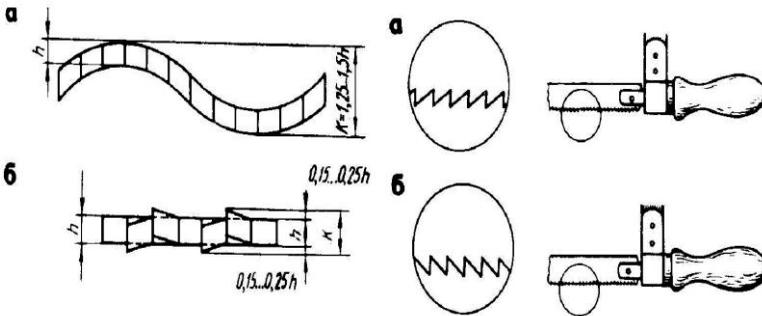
Схема разводки зубьев ножовочного полотна
